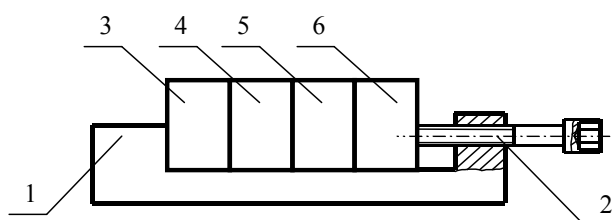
Схема закрепления образцов в струбцине для установки на стол плоскошлифовального станка:
